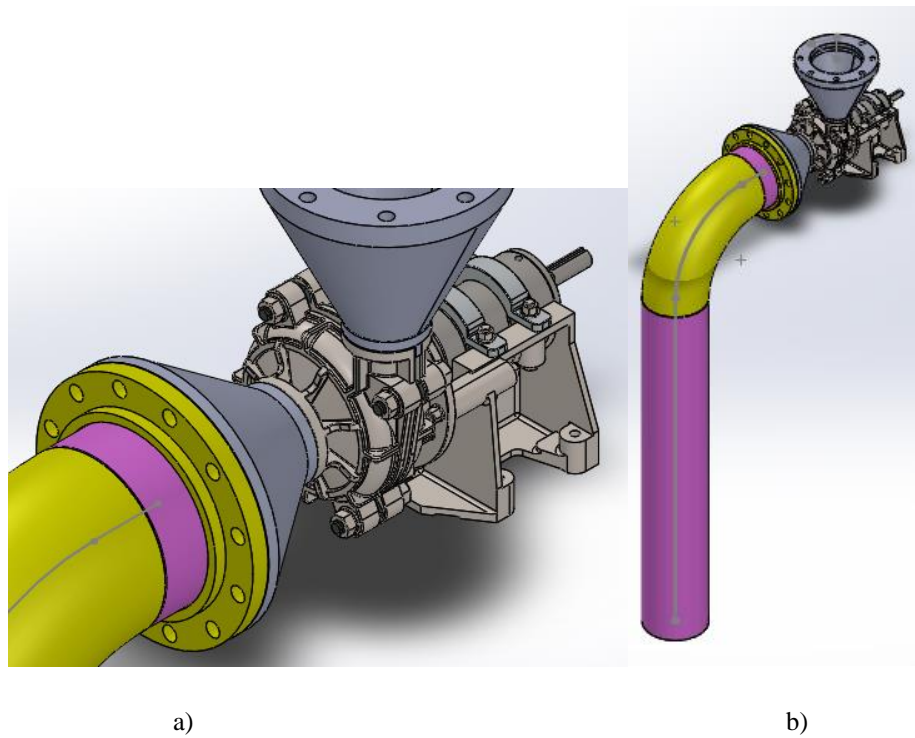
a) Brida de soldadura 10 plg; b) Diseño de tubería de succión.
